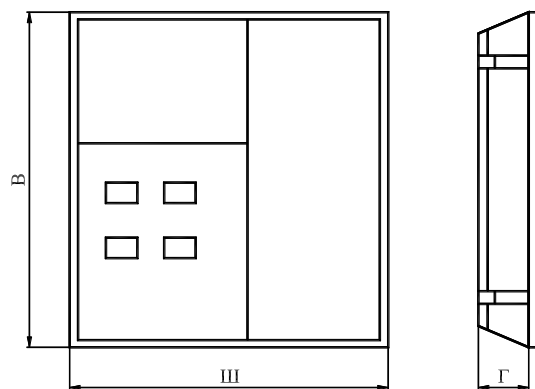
Габаритные размеры корпусов металлических ЩЭ
